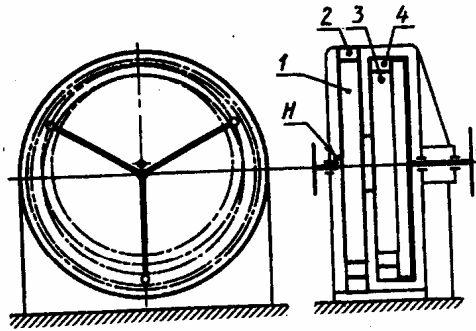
(а). Кинематическая схема планетарного двухступенчатого редуктора с ведущим водилом:
